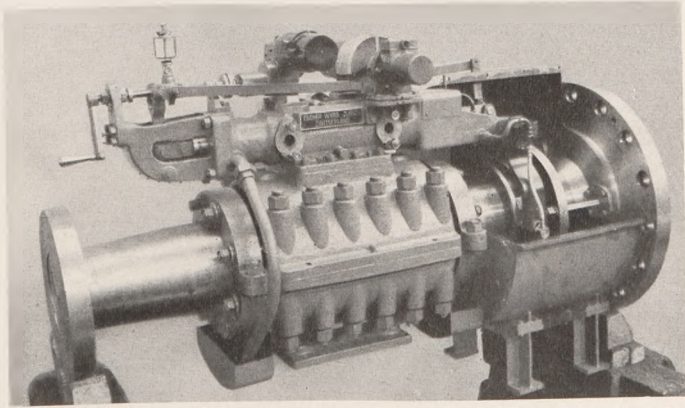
Druckölzuführung mit elektrisch verstellbarem Steuerventil.
